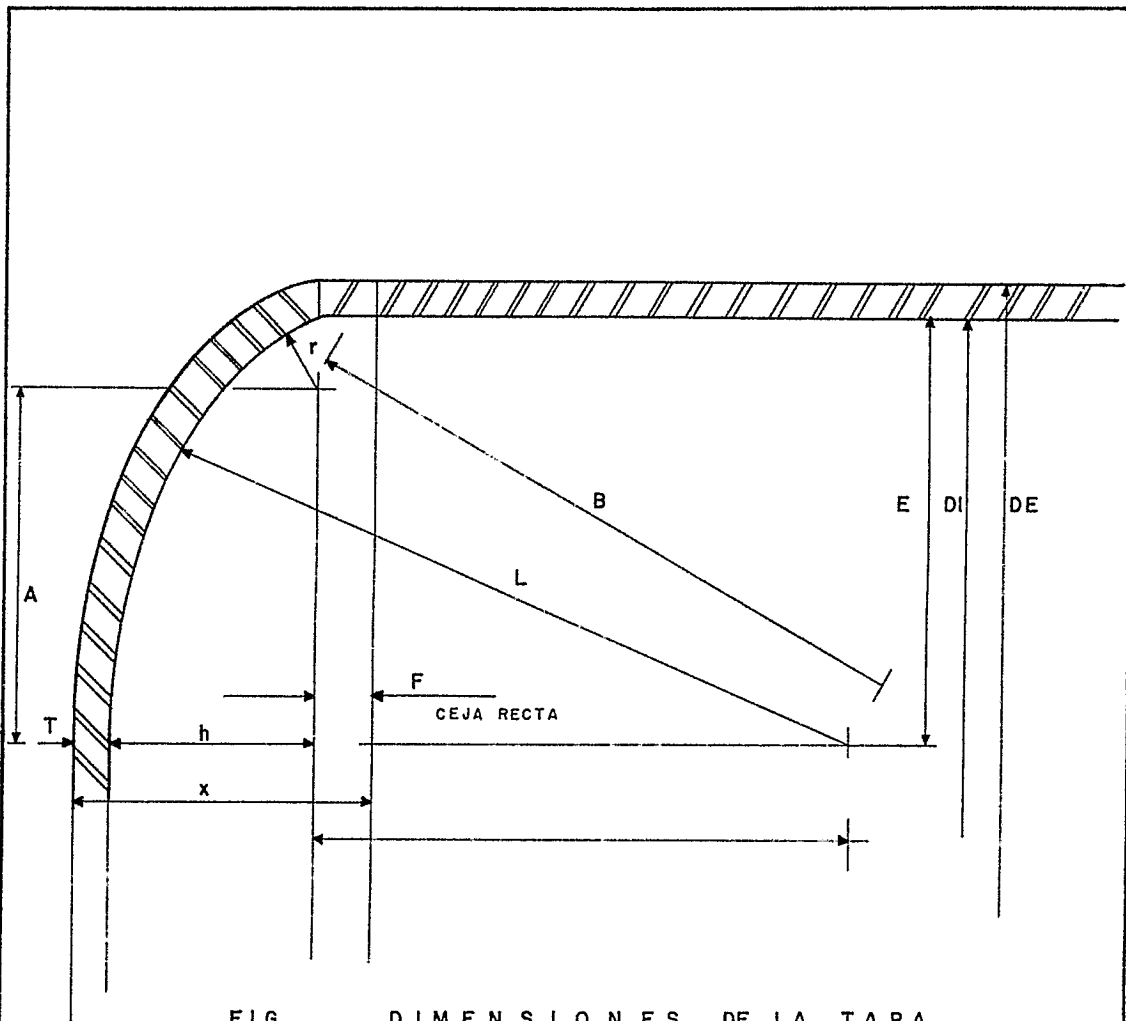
FIG. DIMENSIONES DE LA TAPA TORIESFERICA
